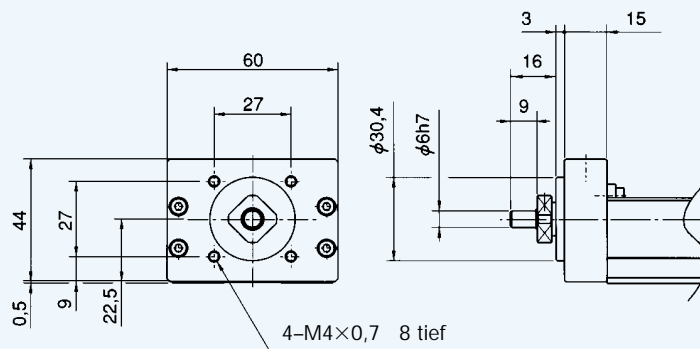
KR33 Housing A ohne Motorflansch (Kennziffer □□40)
